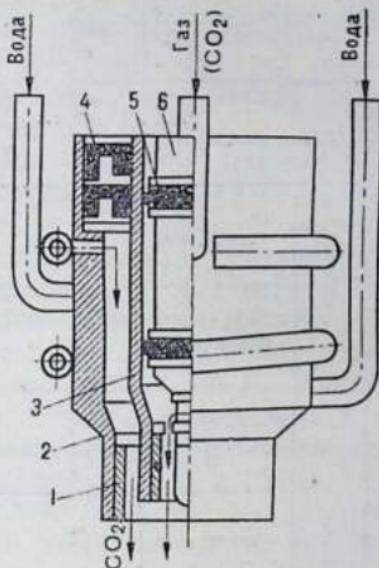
Горелка для комбинированной защиты сварочной дуги при наплавке:
